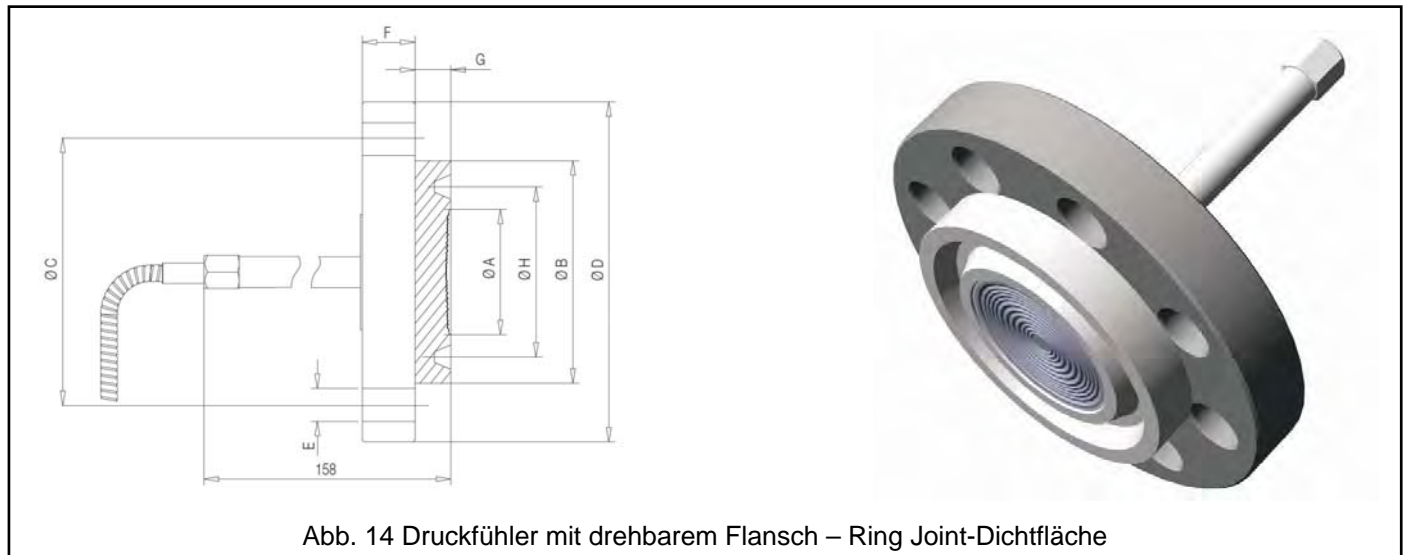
Druckfühler mit drehbarem Flansch – Ring Joint-Dichtfläche
